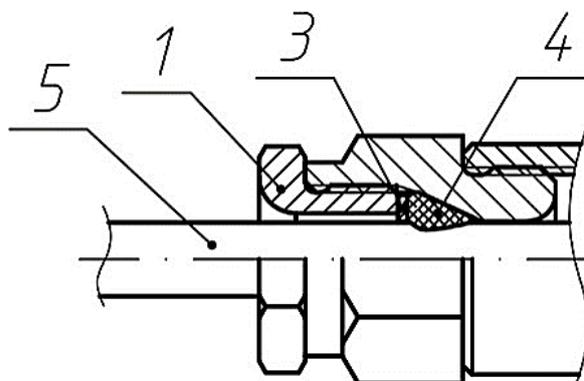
Кабельный ввод для открытой прокладки кабеля К10 и К14 с проложенным кабелем
